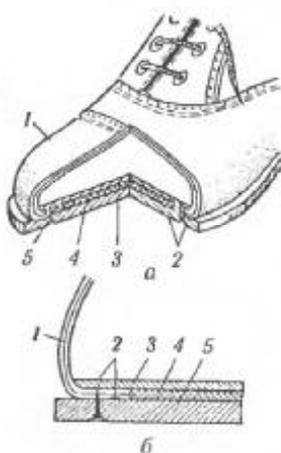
Гвинтово-цвяхове кріплення: а — розріз взуття; б — схема кріплення; 1 — заготівка; 2 — цвяхи; 3 — устілка; 4 — прокладка; 5 — підшва
